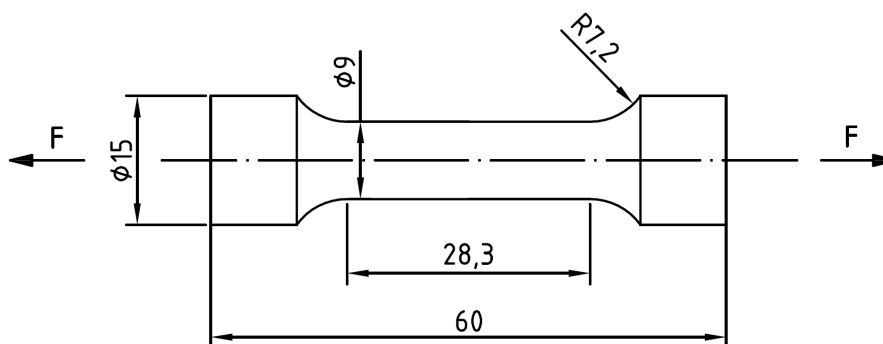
Geometria e direção de carregamento do provete axissimétrico não-entalhado. Dimensões em mm.
